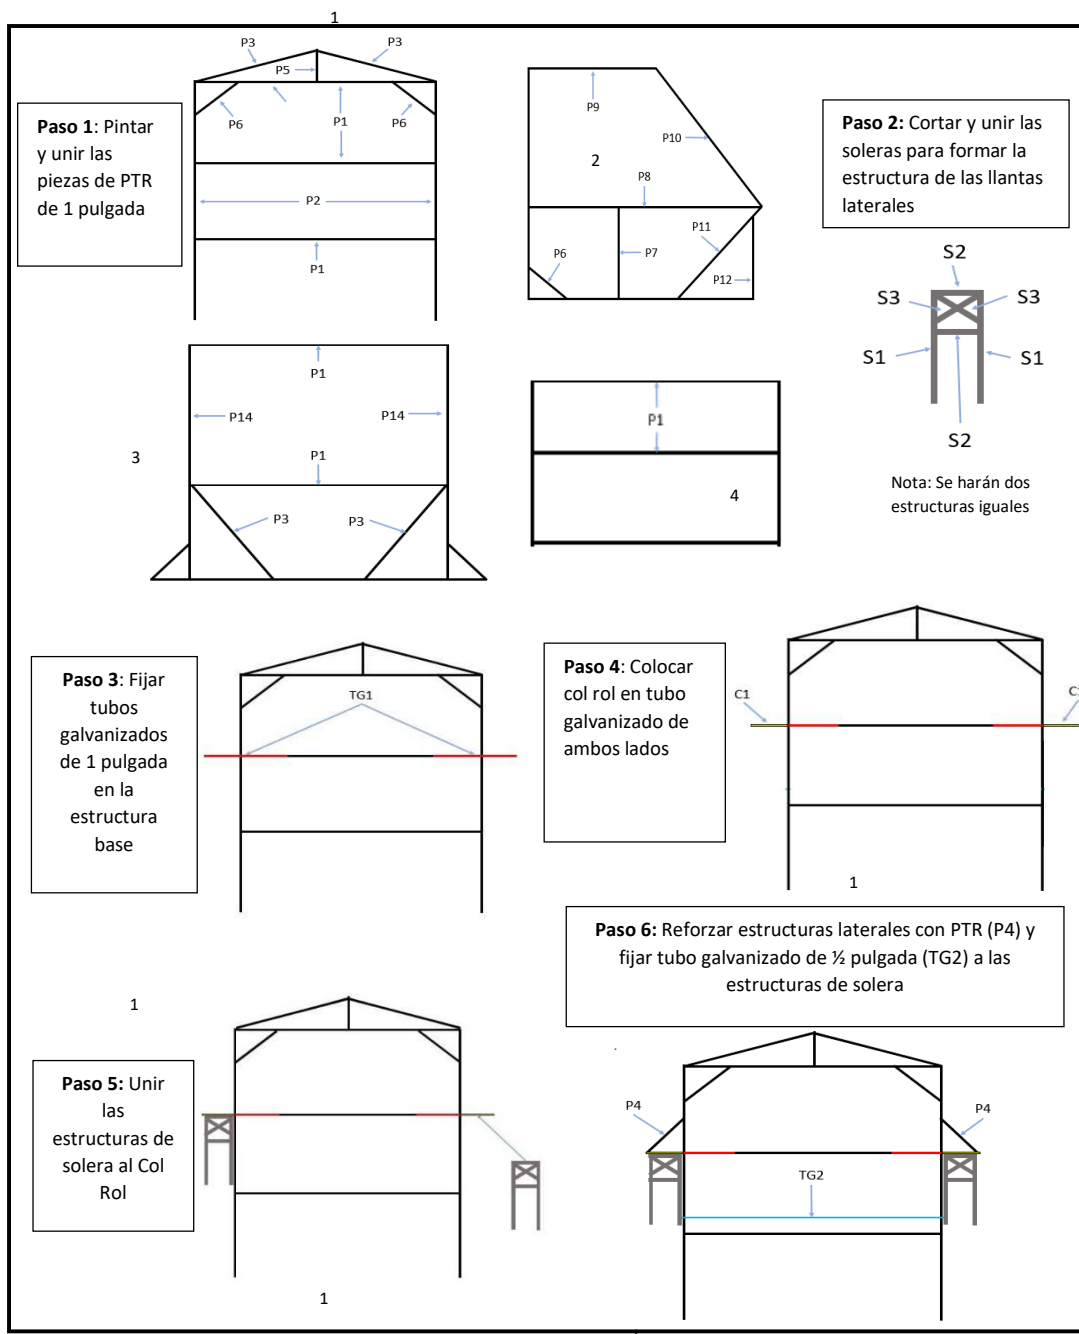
Instructivo de armado de Carreta, Parte 1. Fuente: Elaboración propia.
